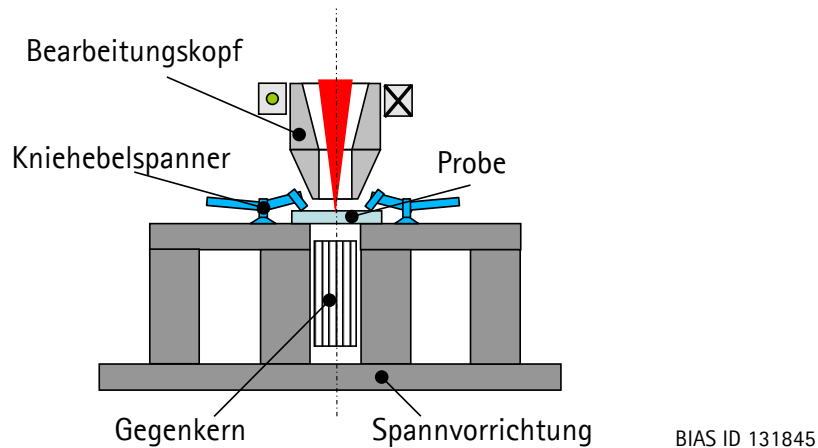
Bearbeitungskopf bestehend aus Schweißoptik und magnetischer Vorrichtung.
